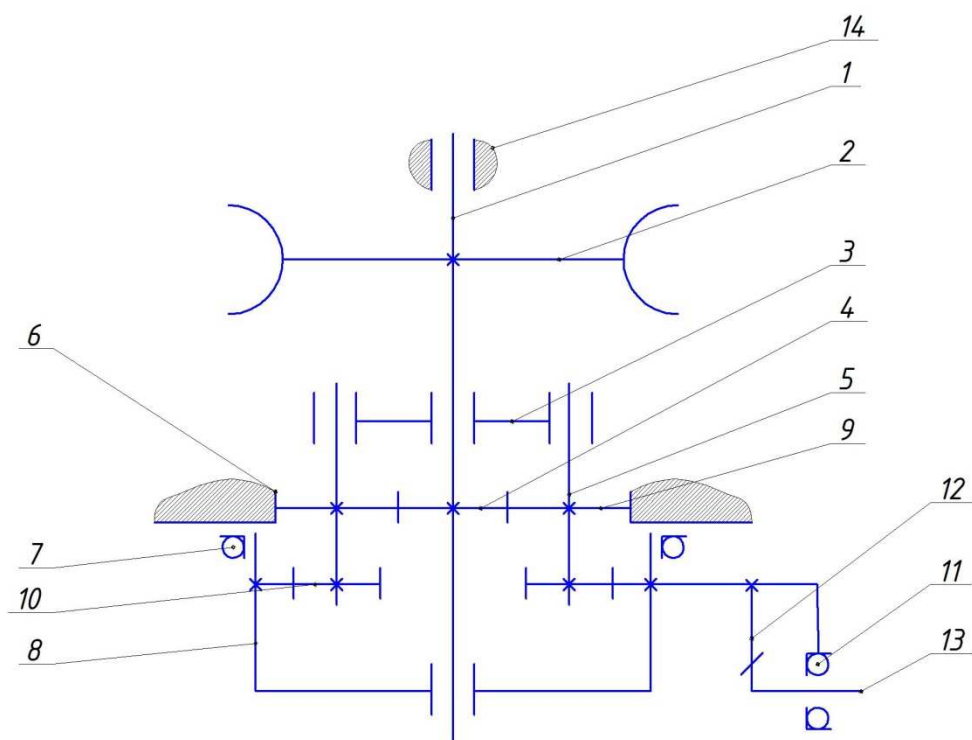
Кінематична схема ротаційної мийної головки: 1 – вал; 2 – турбіна; 3 – водило; 4 – сонячна шестірня; 5 – вісь сателіта; 6 – внутрішній вінець; 7, 11 – підшипники; 8 – рухома частина корпусу головки; 9 – сателітна шестірня; 10 – нижня сателітна шестірня; 12 – конічна шестірня; 13 – вісь форсунок; 14 – корпус ротаційної головки.
